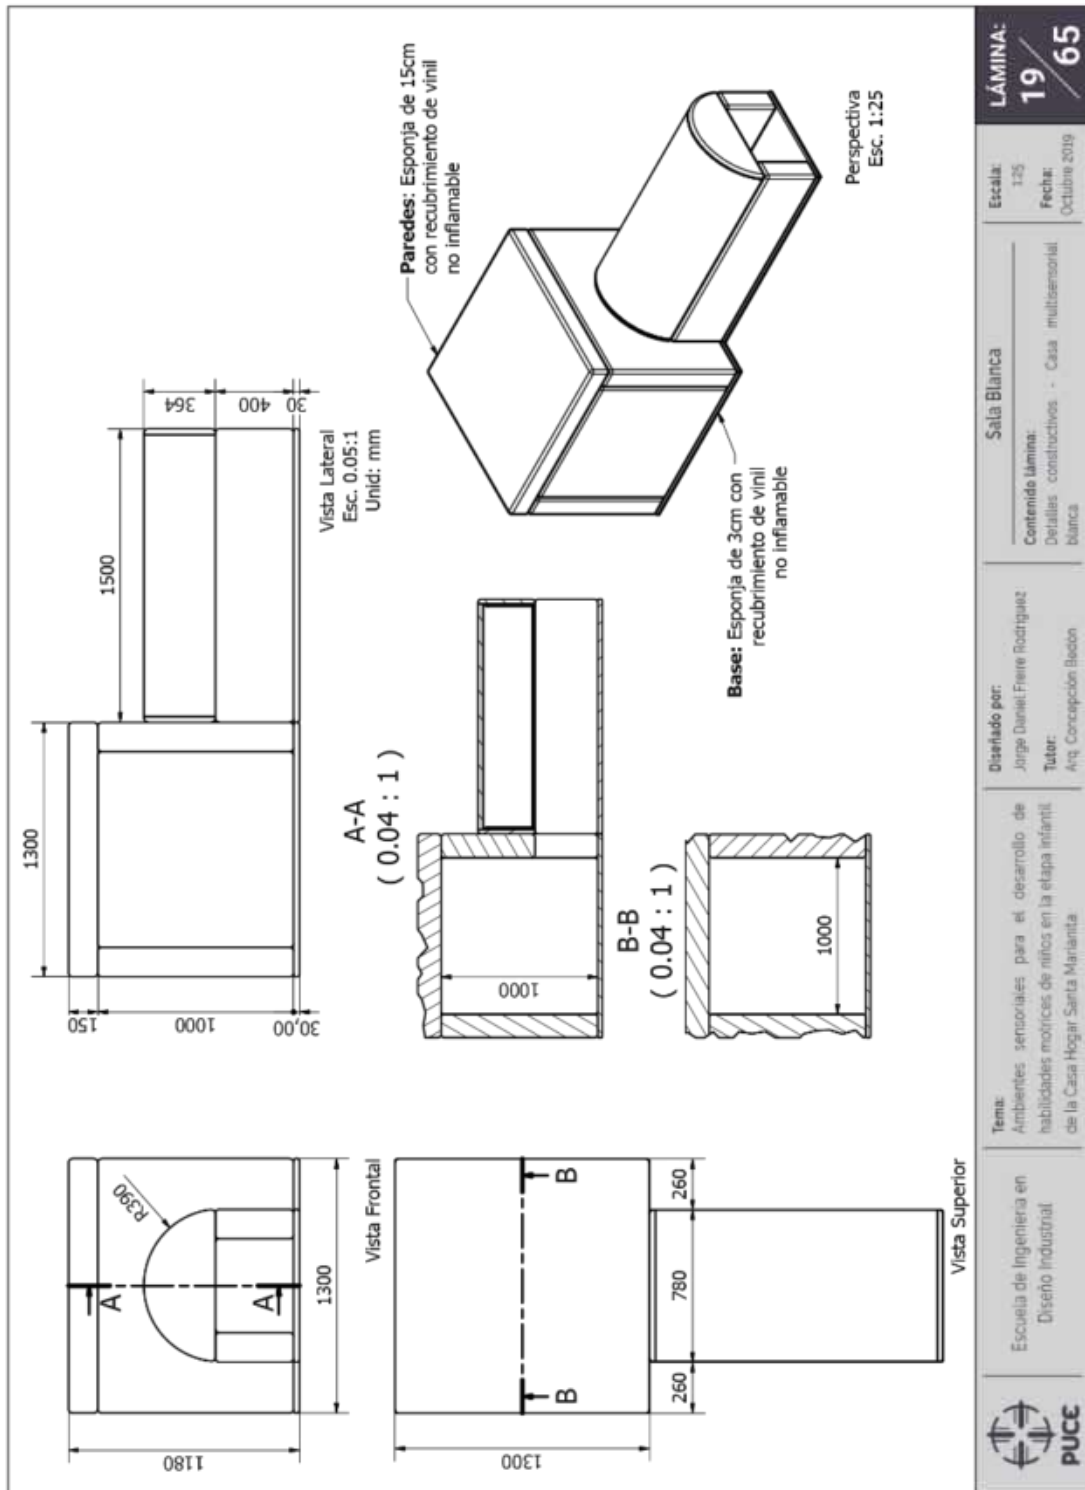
Sala blanca - Detalles constructivos - Mueble vertical tipo globo aerostático
